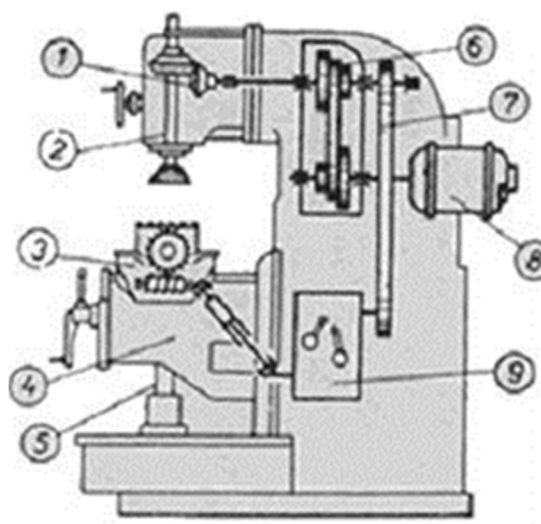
Principais elementos de máquinas da fresadora.
